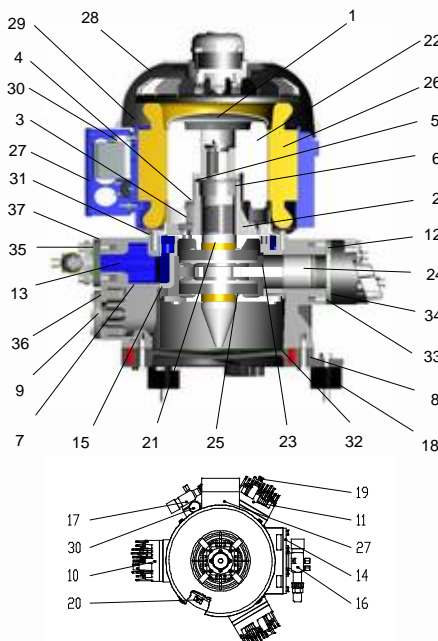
dessin en coupe avec la pompe interne d'huile PI Construction
